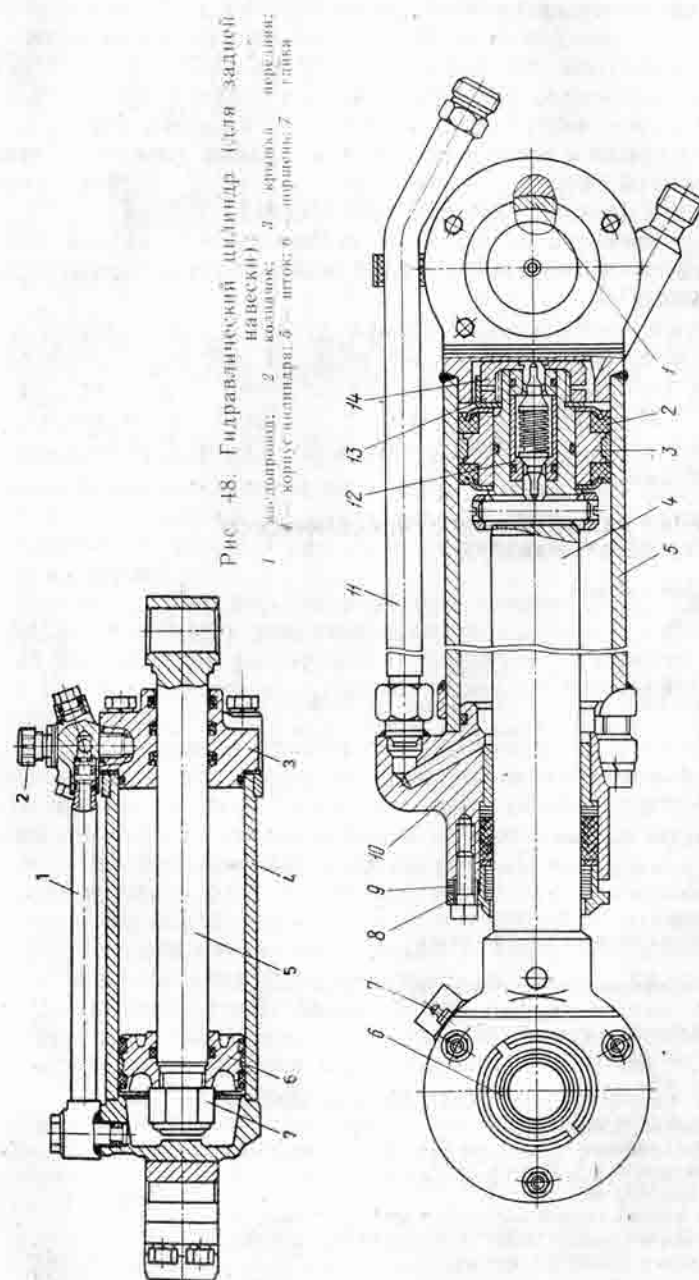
Гидравлический цилиндр (для задней навески): 1 — маслопровод; 2 — козырек; 3 — крышка передняя; 4 — корпус цилиндра; 5 — шток; 6 — поршень; 7 — гайка
